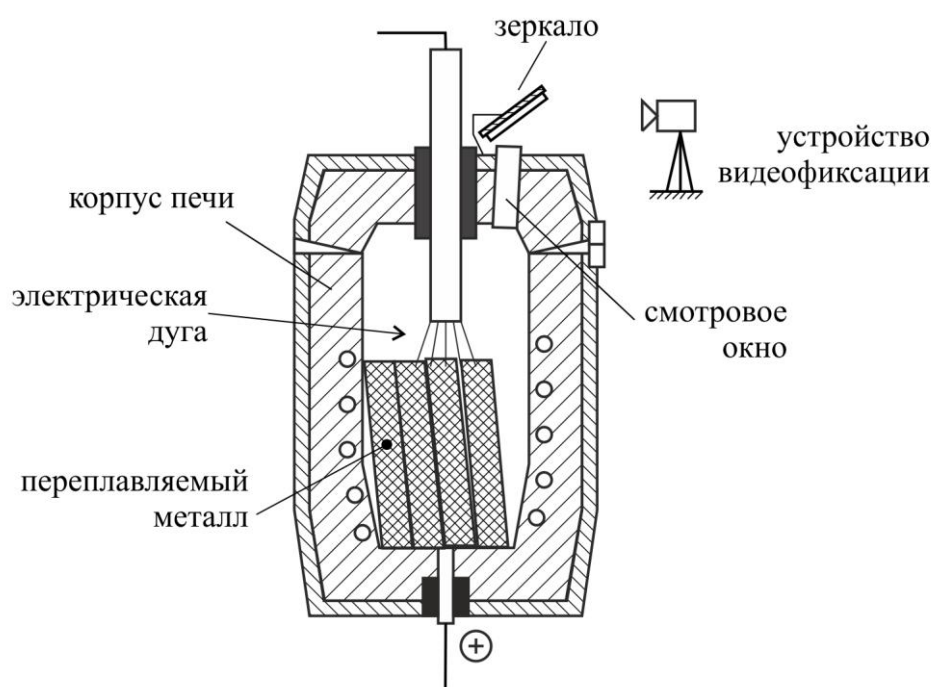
Расположение оборудования при съемке поверхности металла
